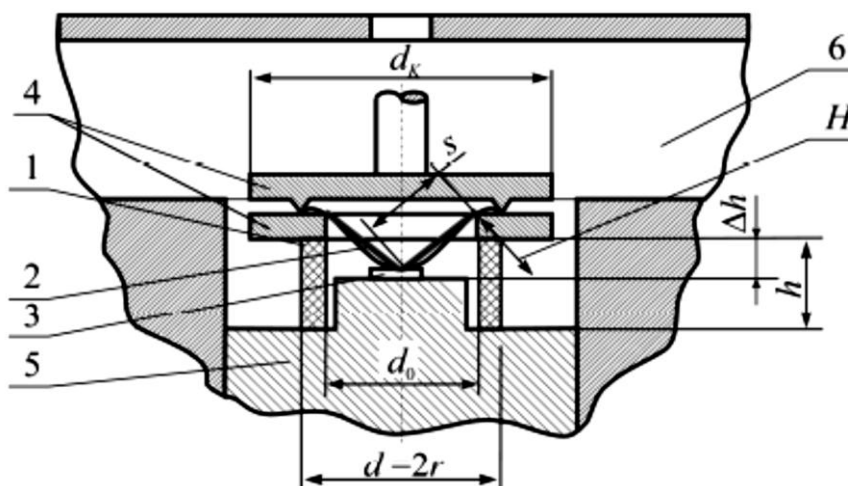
Конструкція напівпровідникового діода в металокерамічному корпусі
